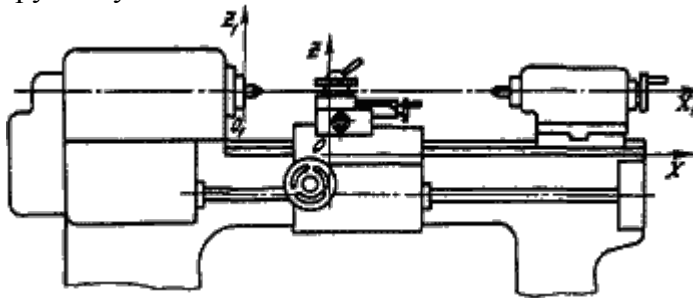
Система прямоугольных координат токарно-винторезного станка
